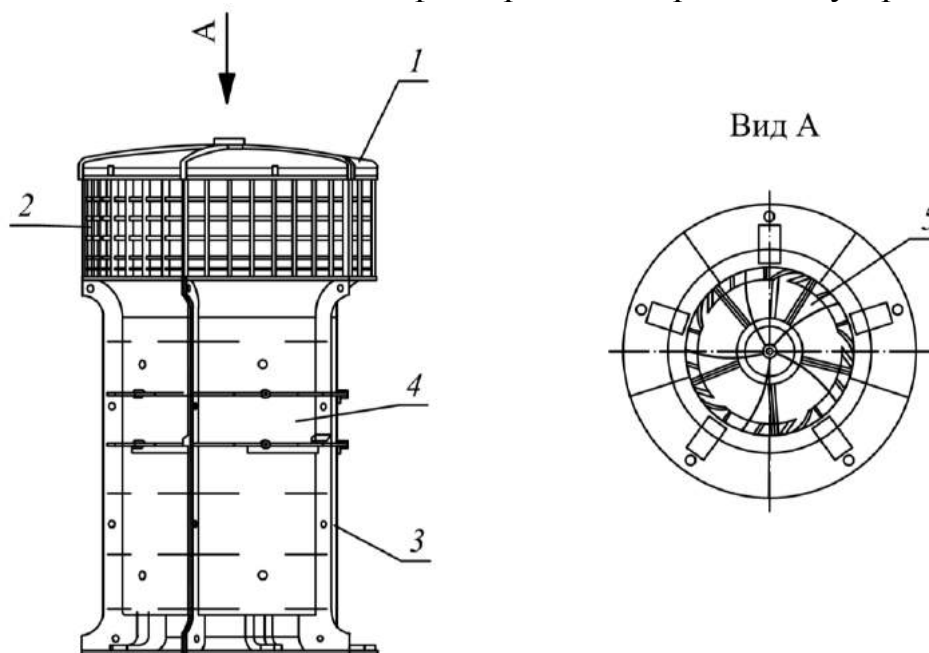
Гибридный вентилятор в сборке: 1 – колпак; 2 – решетка; 3 – разъемное соединение; 4 – цилиндрический корпус; 5 – лопасти вентилятора
